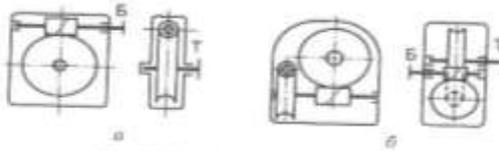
Червячные редукторы: а — одноступенчатый с верхним расположением червяка; б — двухступенчатый
